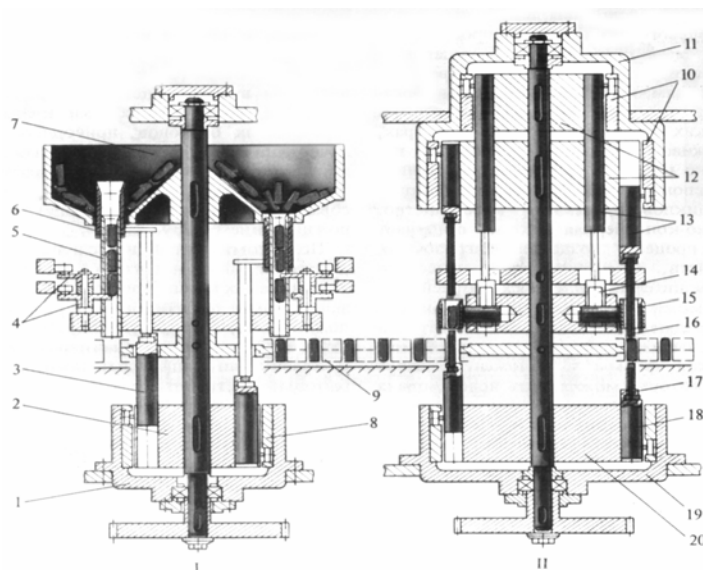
Роторно-конвейерное загрузочное устройство: I–ротор поштучного захвата предметов обработки; II–ротор ориентации предметов обработки; 1 – стакан; 2 – барабан; 3 – ползун; 4 – отсекатели; 5 – накопитель; 6 – захватный орган; 7 – бункер; 8 – цилиндрический кулачок; 9 – транспортный конвейер; 10– кулачки; 11 – стаканы; 12 – барабаны; 13 – ползуны; 14 – зубчатая рейка; 15 – ориентатор; 16 – выталкиватель; 17 – поддерживатель
